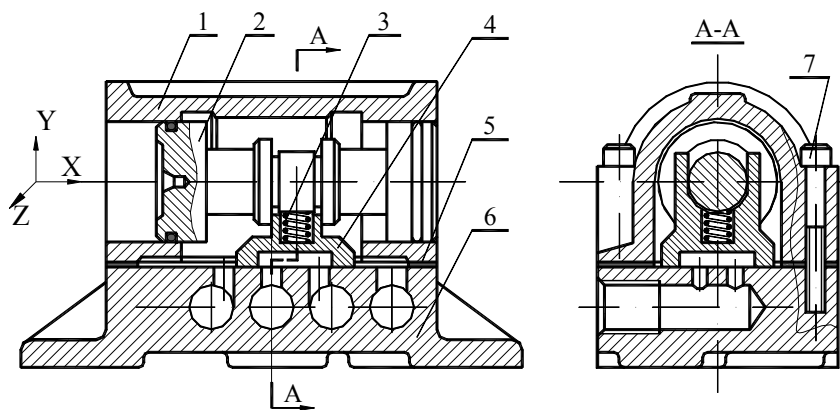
Реверсивний пневматичний золотник: 1 – циліндр; 2 – двосторонній поршень; 3 – пружина; 4 – золотник; 5 – прокладка; 6 – основа; 7 – гвинти
